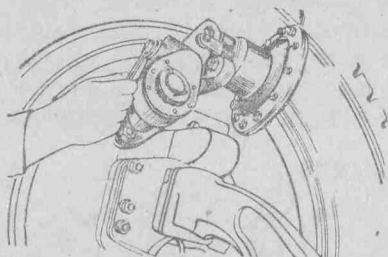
Регулировка колесного тормоза с помощью червяка тормозной камеры
